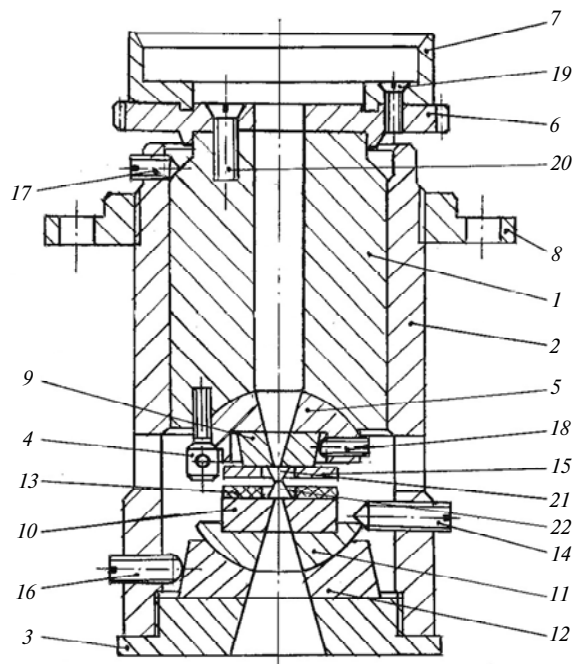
Схема SDAC: 1 – подвижный поршень; 2 – корпус; 3 – дно; 4 – винт; 5 – опора полусферическая верхняя; 6 – колесо зубчатое; 7 – лимб; 8 – фланец; 9 – опора верхняя; 10 – опора нижняя; 11 – опора полусферическая нижняя; 12 – опора полусферическая; 13 – пластина текстолитовая; 14 – винт; 15 – пластина стальная; 16–20 – винт; 21 – подвижная АН; 22 – неподвижная АН.
